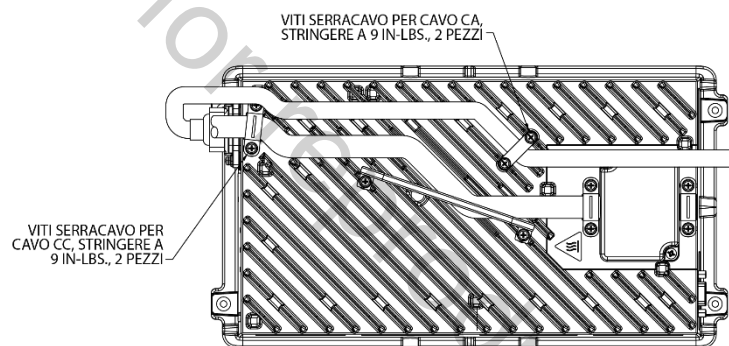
Instradamento alternativo dei cavi CA e CC
